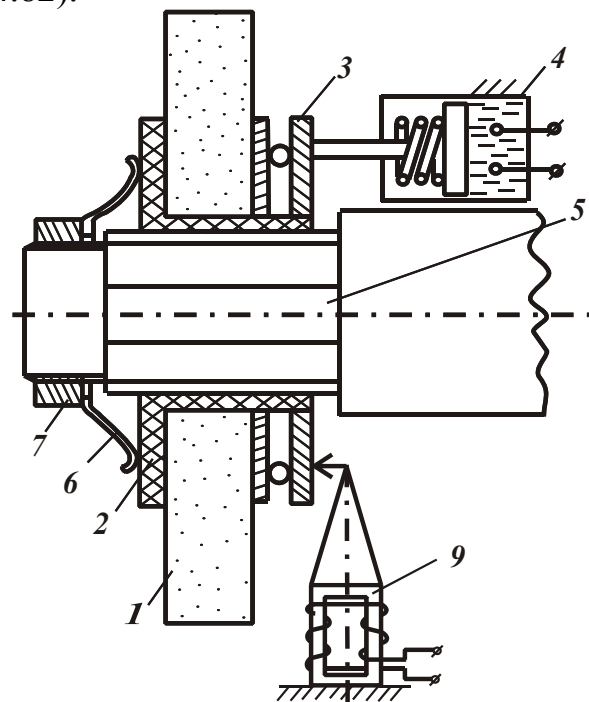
Устройство для абразивно-шлифовальной обработки с перемещением круга гидравлическими ударами от электрических разрядов с магнито-стрикционной колебательной системой: 1 – круг; 2 – шлицевая втулка; 3 – подшипник; 4 - гидравлический цилиндр с поршнем-штоком, возвратной пружиной, электродами для гидравлического удара; 5 – шлицевый вал; 6 – пружина; 7 – гайка; 8 – эксцентрик; 9 – магнито-стрикционная колебательная система.
